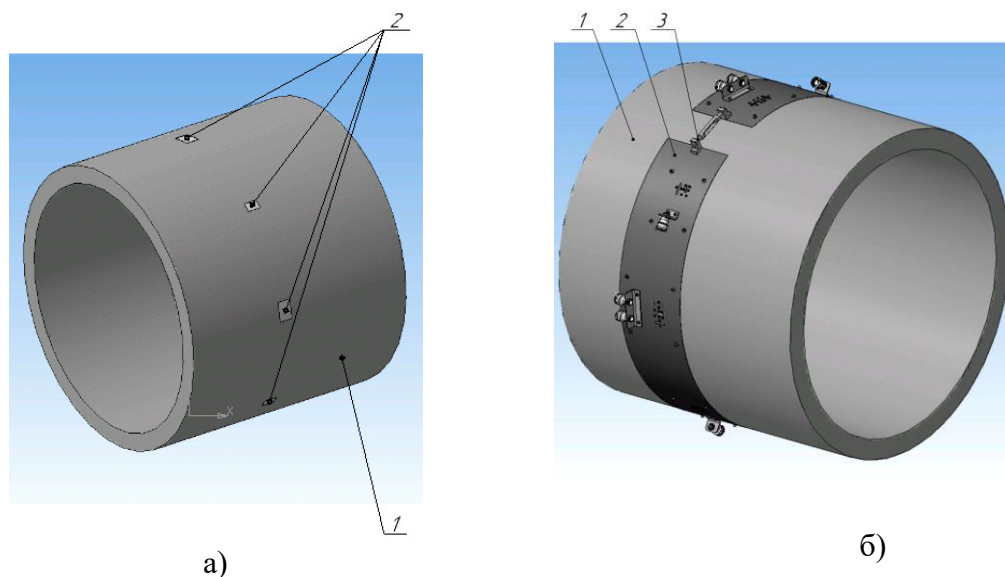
Внешний вид подготовленного к монтажу трубопровода (а) и установленного шаблона (б): 1 – трубопровод; 2 – места обработки трубопровода; 3 – шаблон; 4 – талреп
